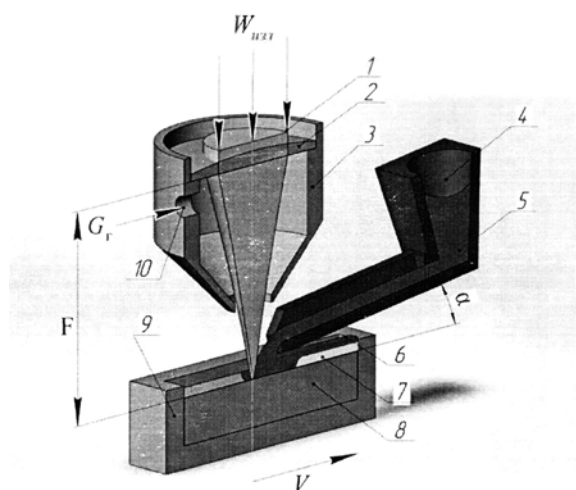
Технологічна схема лазерно-ливарного методу виготовлення біметалів: 1 - лазерне випромінювання; 2 - лінза; 3 - сопло; 4 - лоток; 5 - плакуючий розплав; 6 - поверхневий шар; 7 - твердий шар; 8 - заготовка; 9 - обмежувачі; 10 - захисний газ.
